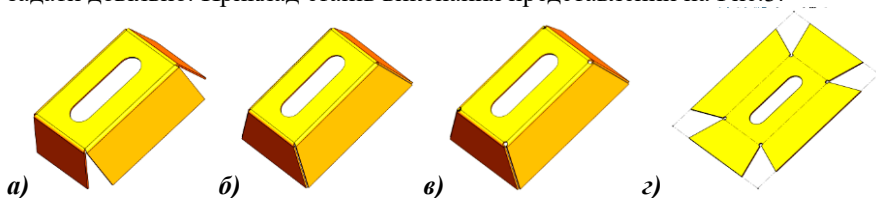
Закриття кута: а) заготовка; б) закриття кутів шляхом їх видовження; в) зняття напруження кутів (тип круглий); г) розгортка
